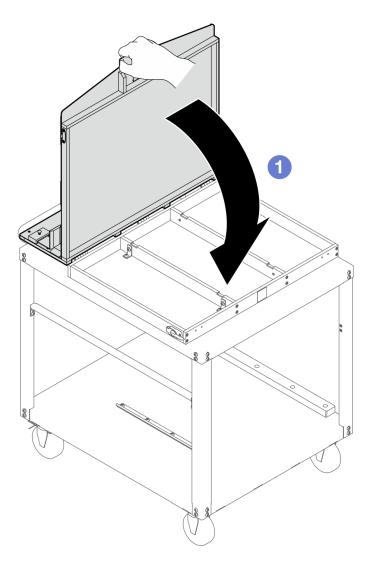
Gire la placa de la estructura giratoria a la posición cerrada.
